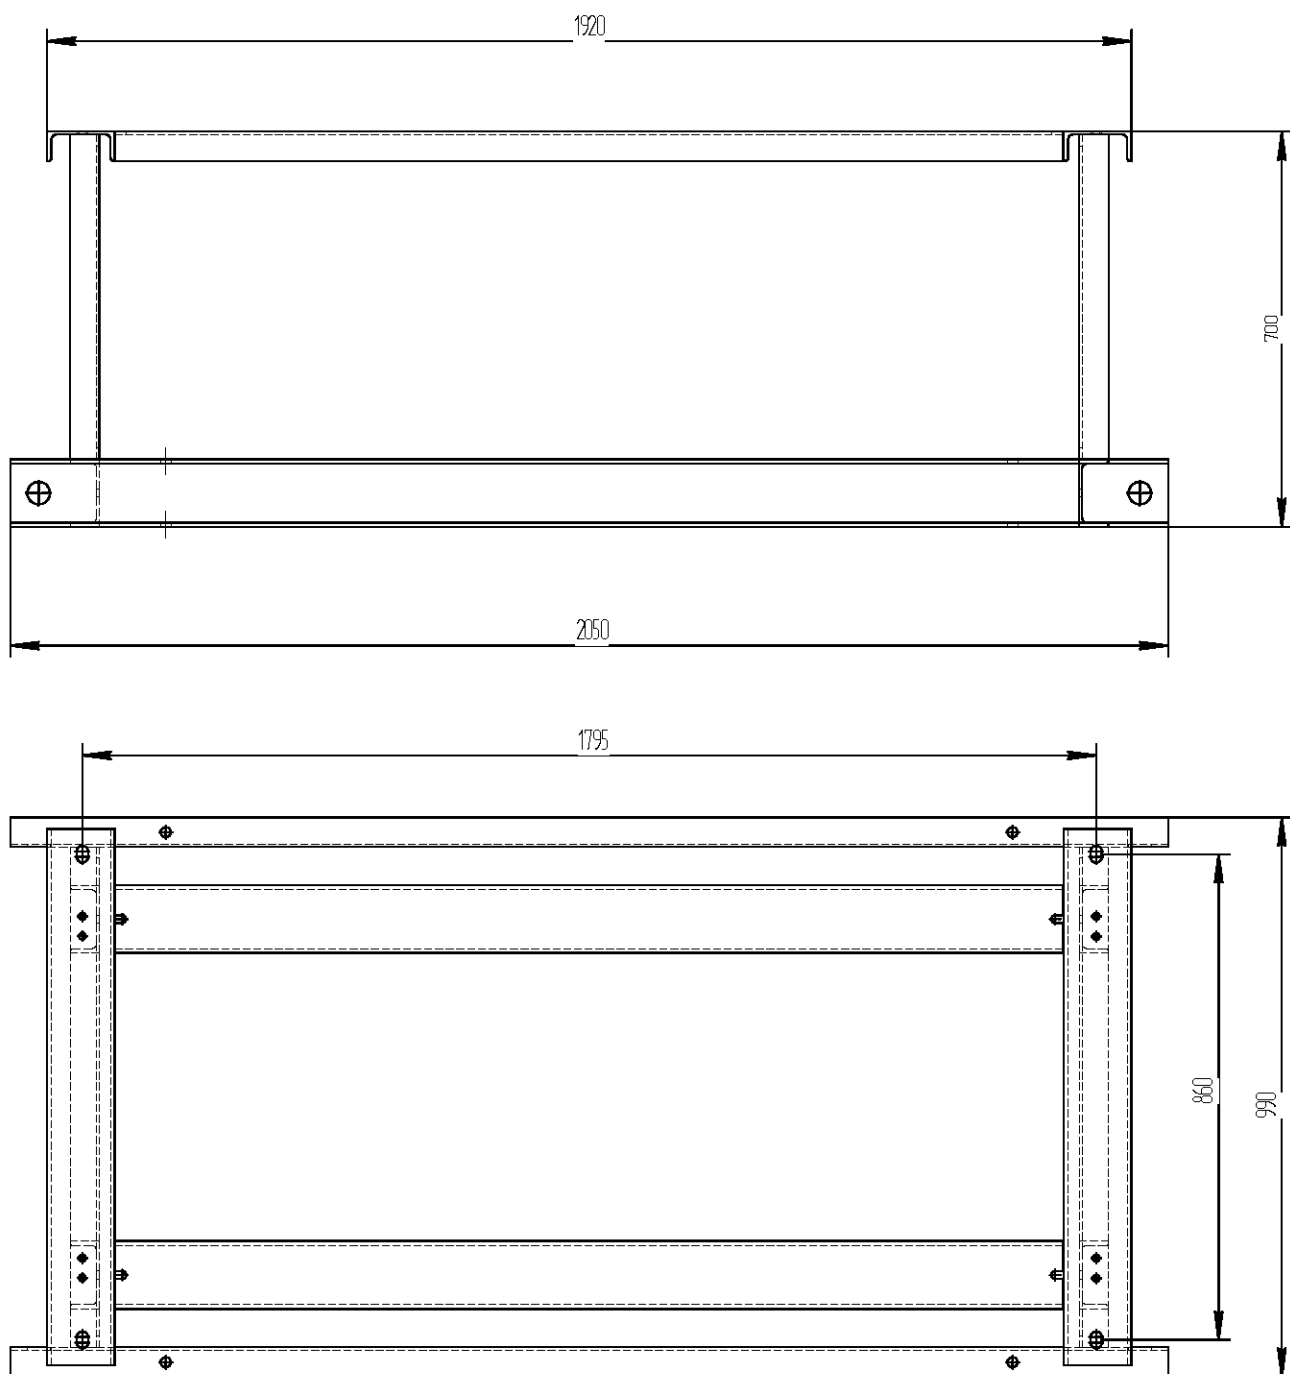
Габаритные и присоединительные размеры подставки
